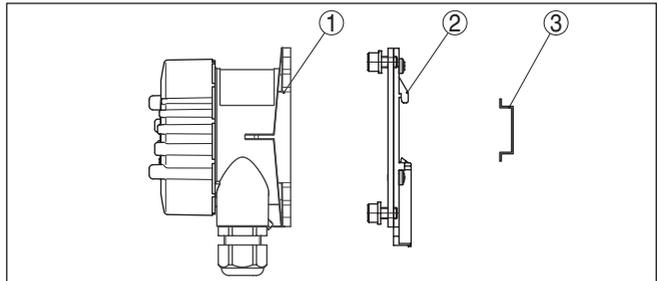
VEGABOX 03 con carcasa de aluminio y acero inoxidable para el montaje en regleta de montaje
